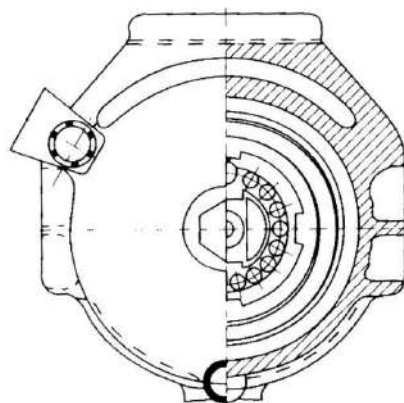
Буксовий вузол з вільною ділянкою у верхньому зводі корпусу
